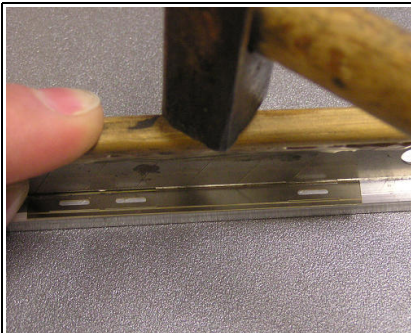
Das Chassis mit der Biegekante genau auf die V-Nut des Aluprofiles legen und mit dem Messer abkanten. (ca.60°möglich)
